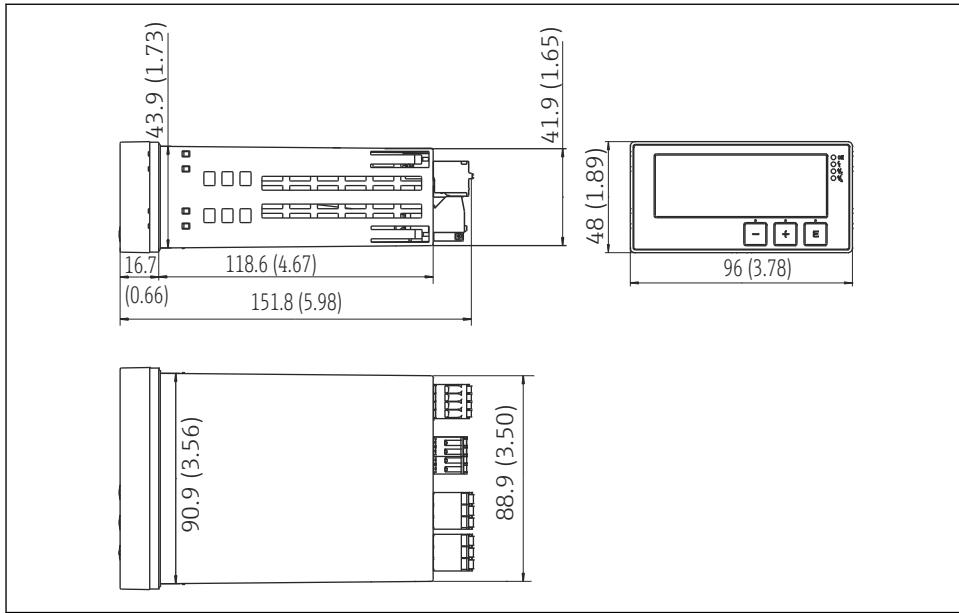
变送器的外形尺寸示意图; 单位: mm (in)
